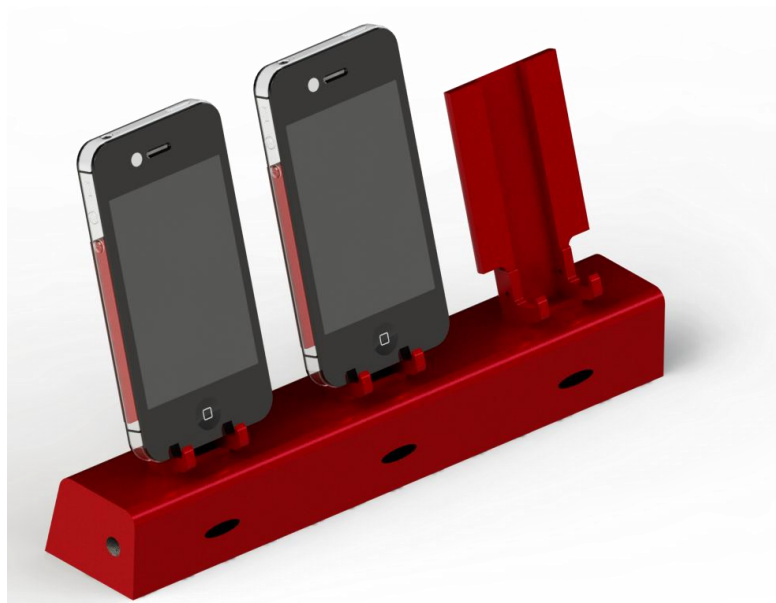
Render final de um conjunto de expositores anexados entre si com ajuda de um suporte magnético
